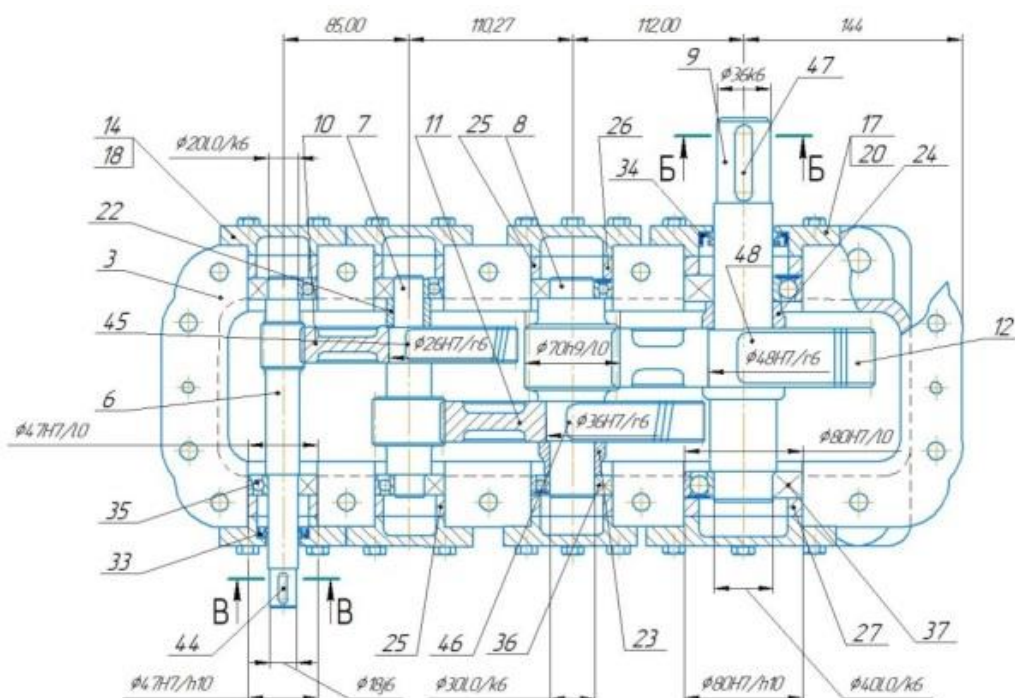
Эскиз редуктора ВК – 490 в разрезе
